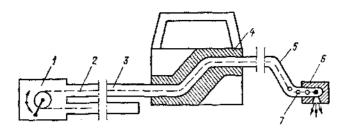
Коиструктивная схема гамма-дефектоскова шлангового типа t= привод; 2= подающий канал; 3= соединительный шланг; 4= радиационнях головка; 5= амиулопровод; 6= коллимирующая головка; 7= держатель источнека издраения
